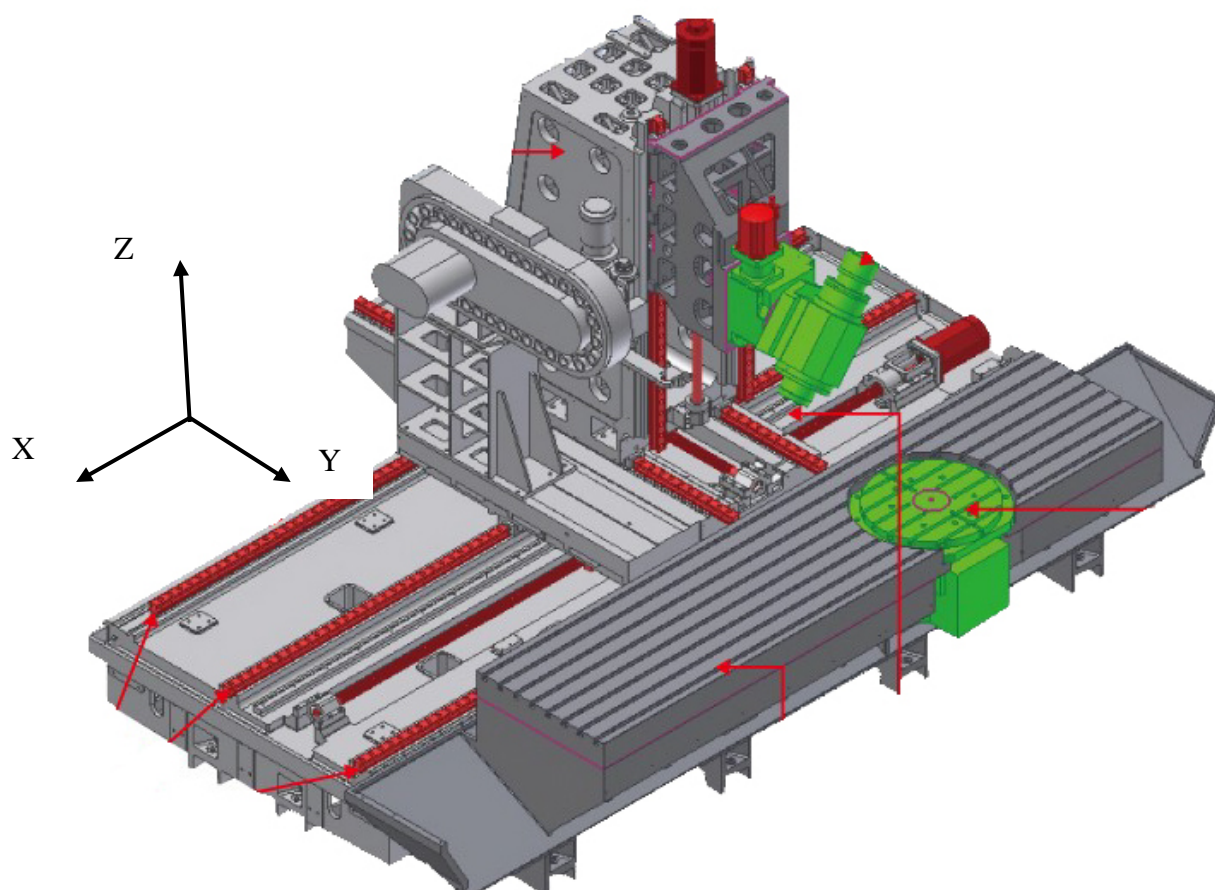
Устройство 5-осевого обрабатывающего центра MV-308-5X
